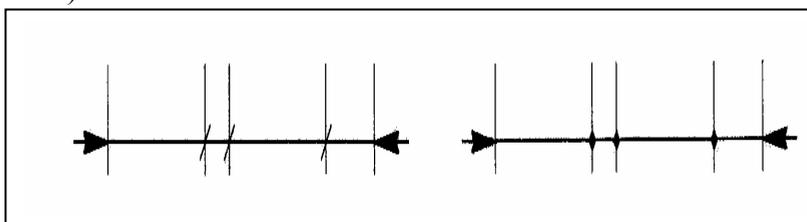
Простановка размеров между смежными элементами (цепочкой)
